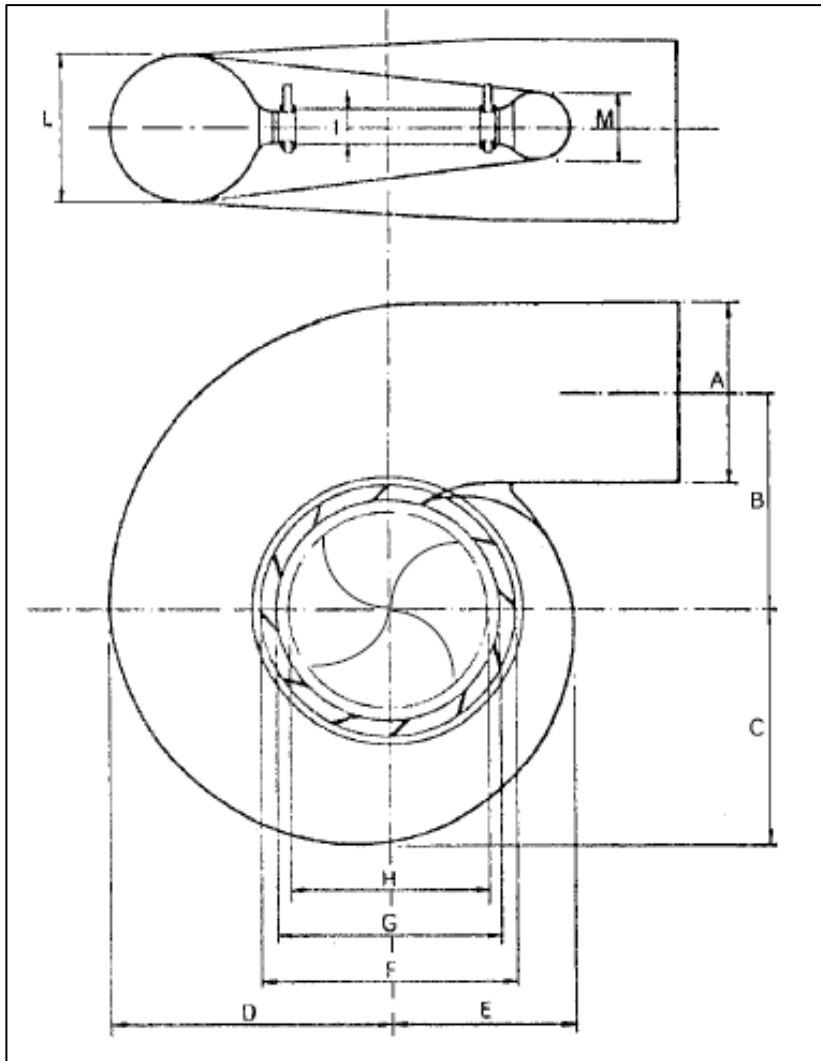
Dimensiones de la carcasa de una turbina tipo Francis
